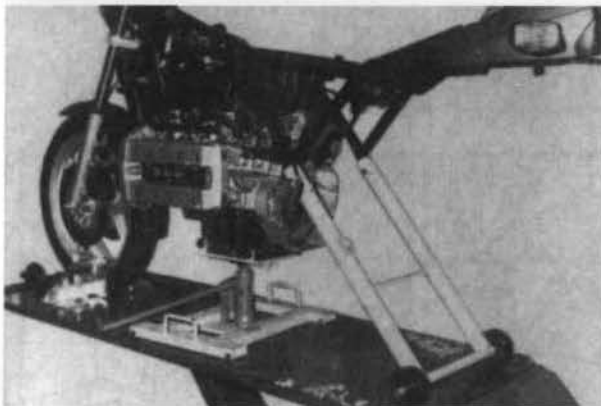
Montaje del caballete con rodillos BMW que debe aguantar la parte trasera de la moto (foto RMT).
